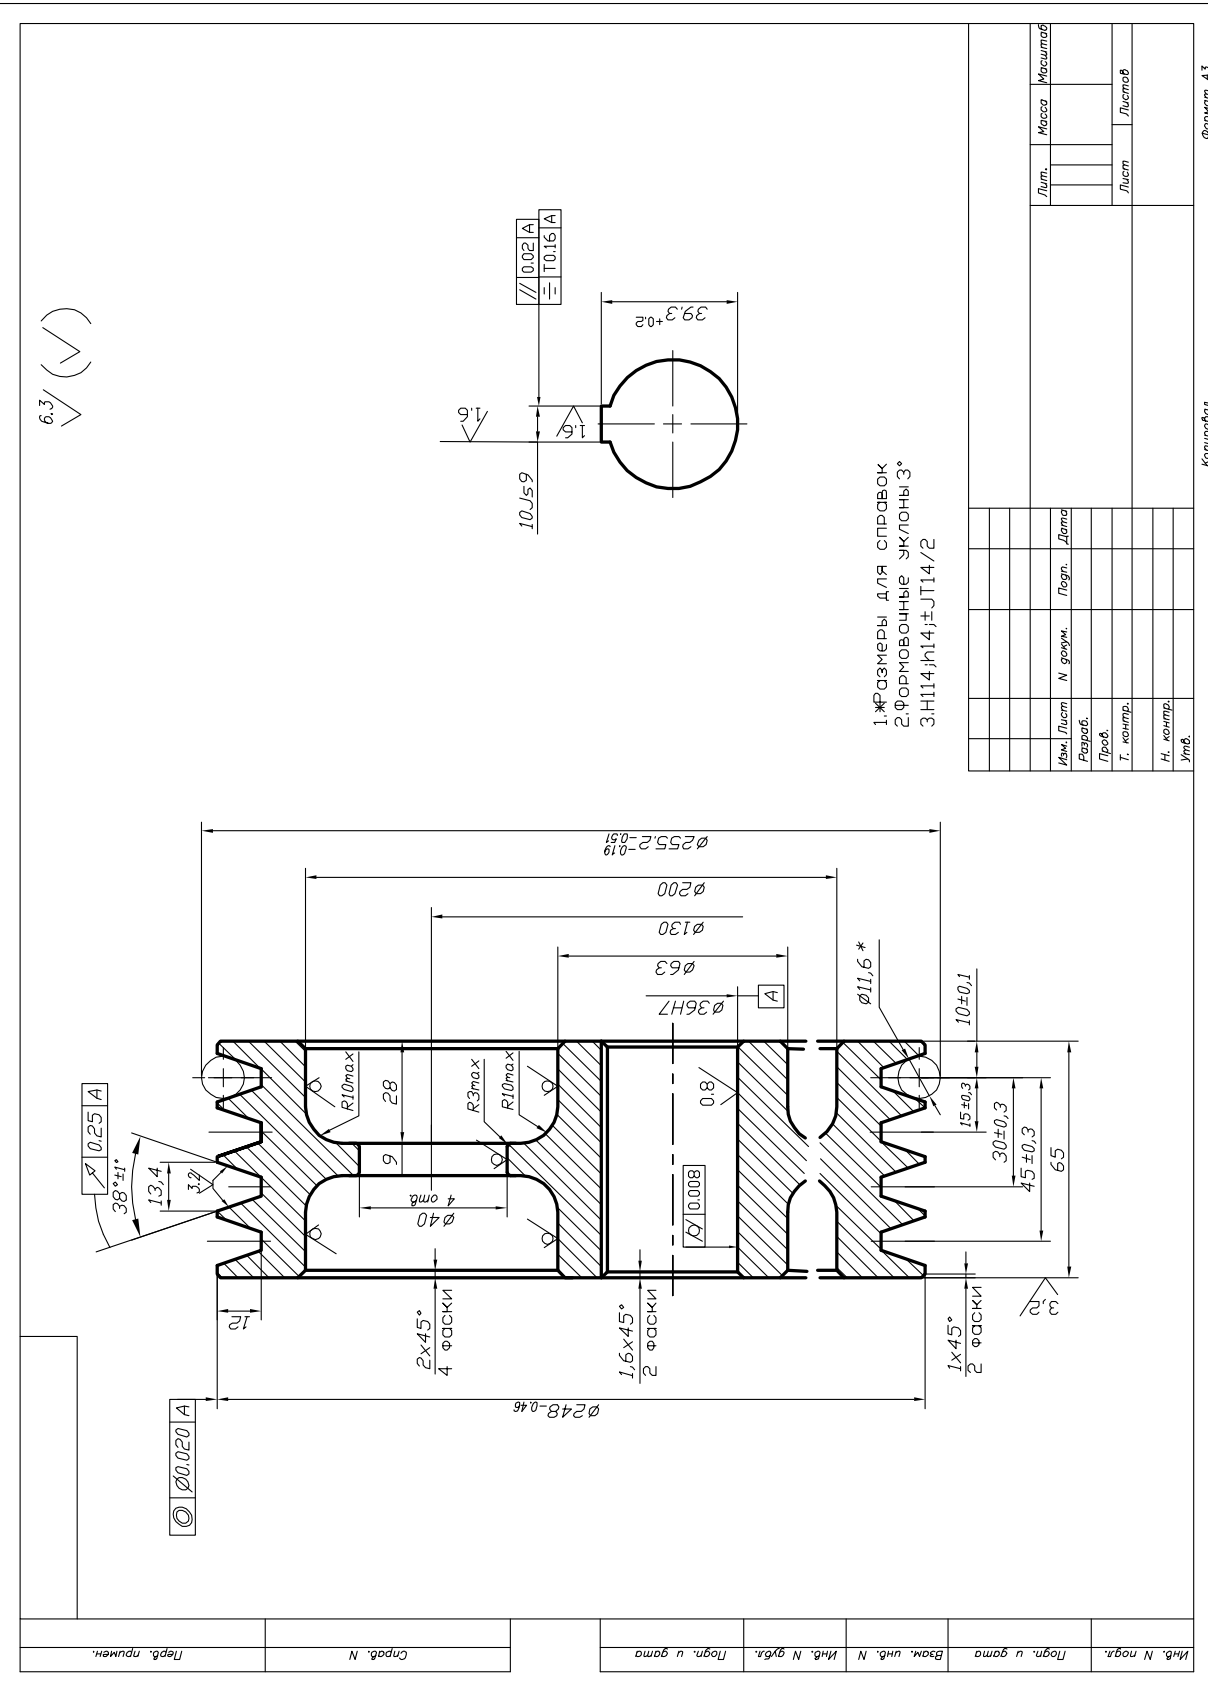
Рабочий чертеж шкива клиноременной передачи
